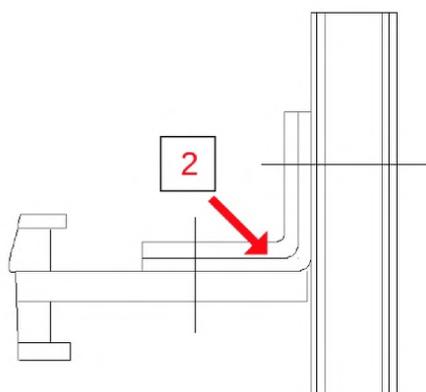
Эскиз крепления укороченного наружного барьера и зона отбора образцов
